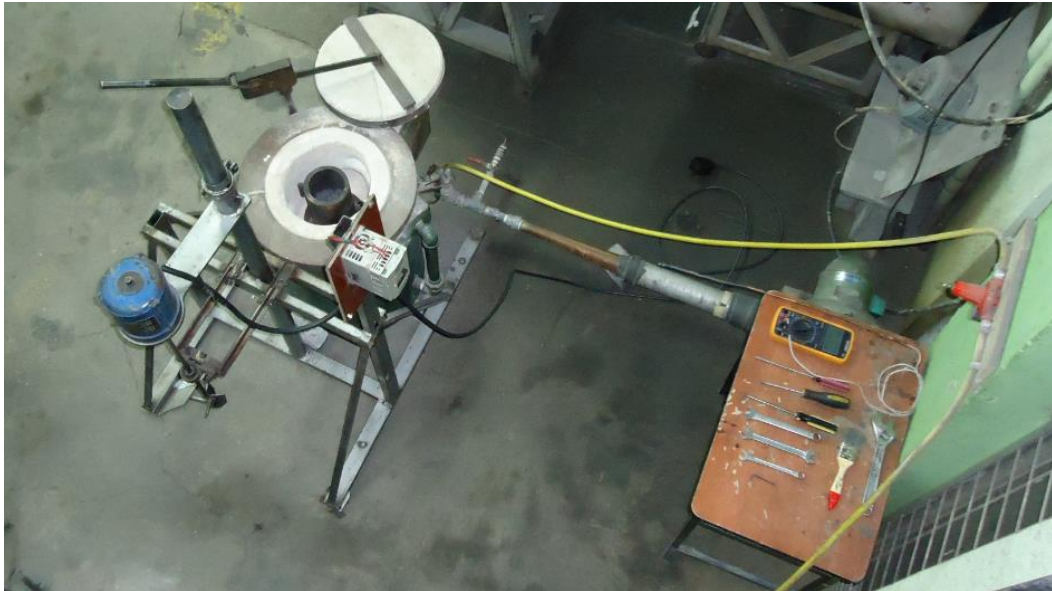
Montaje de los elementos de rotación motor-agitador del stir casting.
